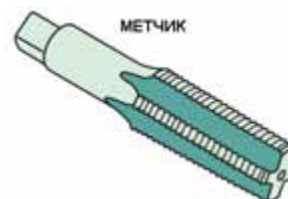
Типичные метчики для чистового прохода используются для нарезания полноценной резьбы в глухих отверстиях, таких как отверстия в блоке цилиндров, используемых для крепления головки цилиндров или крепления крышек коренных подшипников; источник: Pearson Education, Inc.
